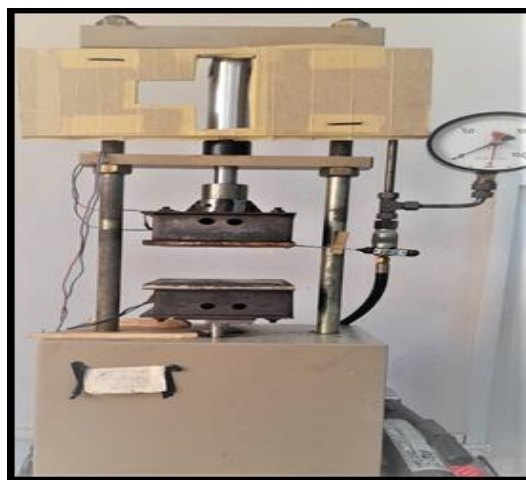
machine manuelle de presse thermo hydraulique.
